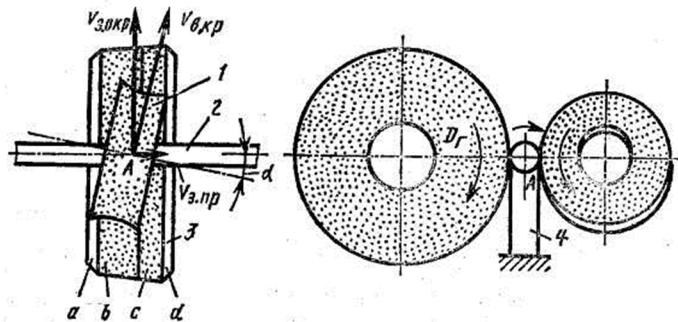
Схема обработки на бесцентрово-шлифовальном станке
